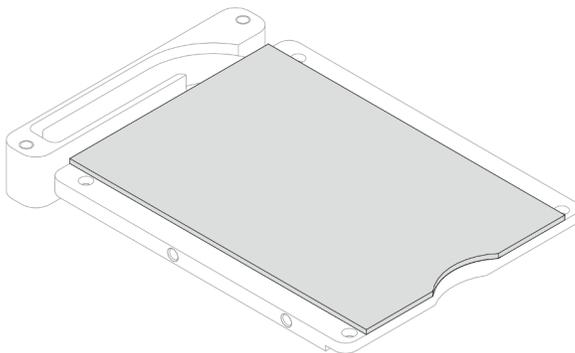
Instalación de la almohadilla de espacio de la placa de conducción
